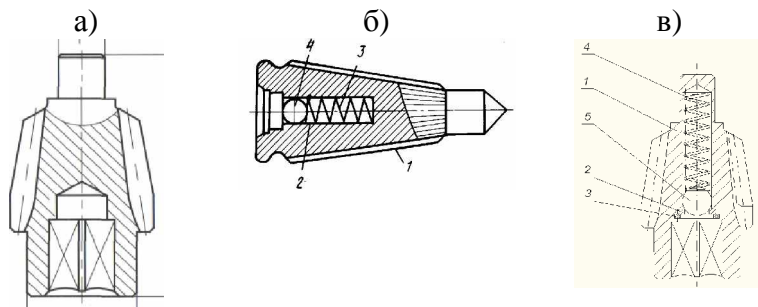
Конические шестерни: а) стандартная коническая шестерня выпускаемая на заводе РУП «БелТАПАЗ»; б) коническая шестерня из патента «RU 2018414 С1 – Шестерня патрона токарного станка»; в) разработанная коническая шестерня. 1 – шестерня; 2 – шайба; 3 – внутреннее эксцентрическое стопорное кольцо; 4 – пружина; 5 – подпружиненный шарик
